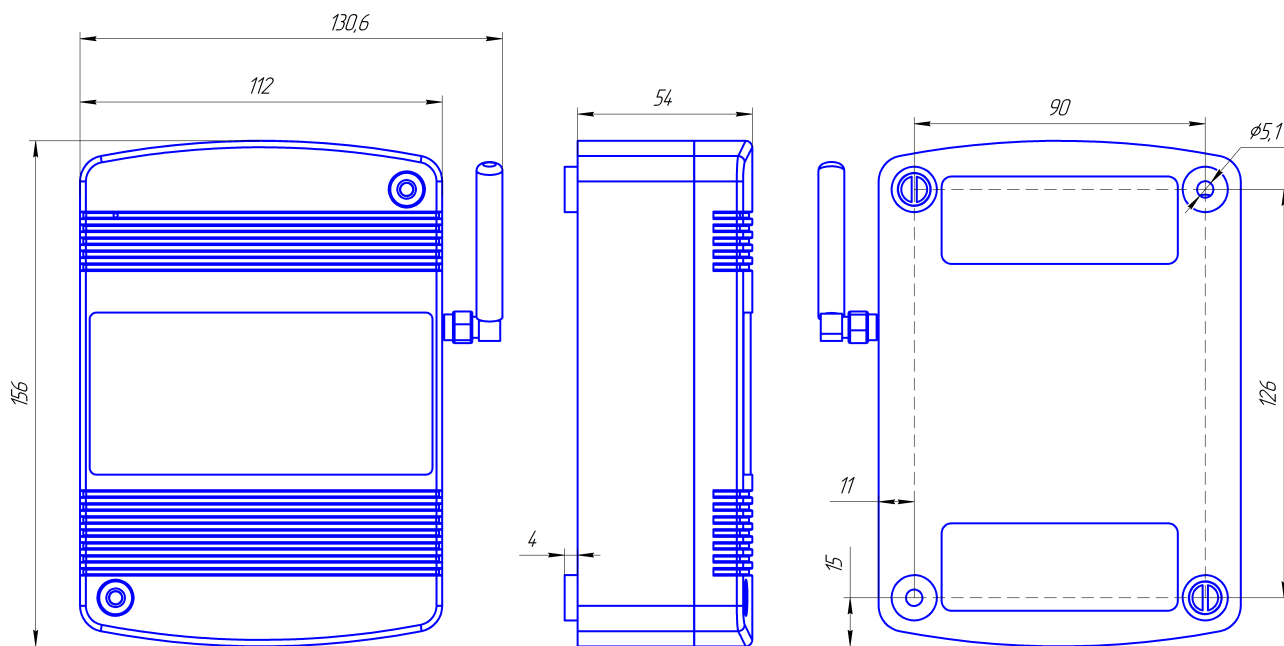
Габаритные и установочные размеры контроллера в исполнении с креплением на стену
